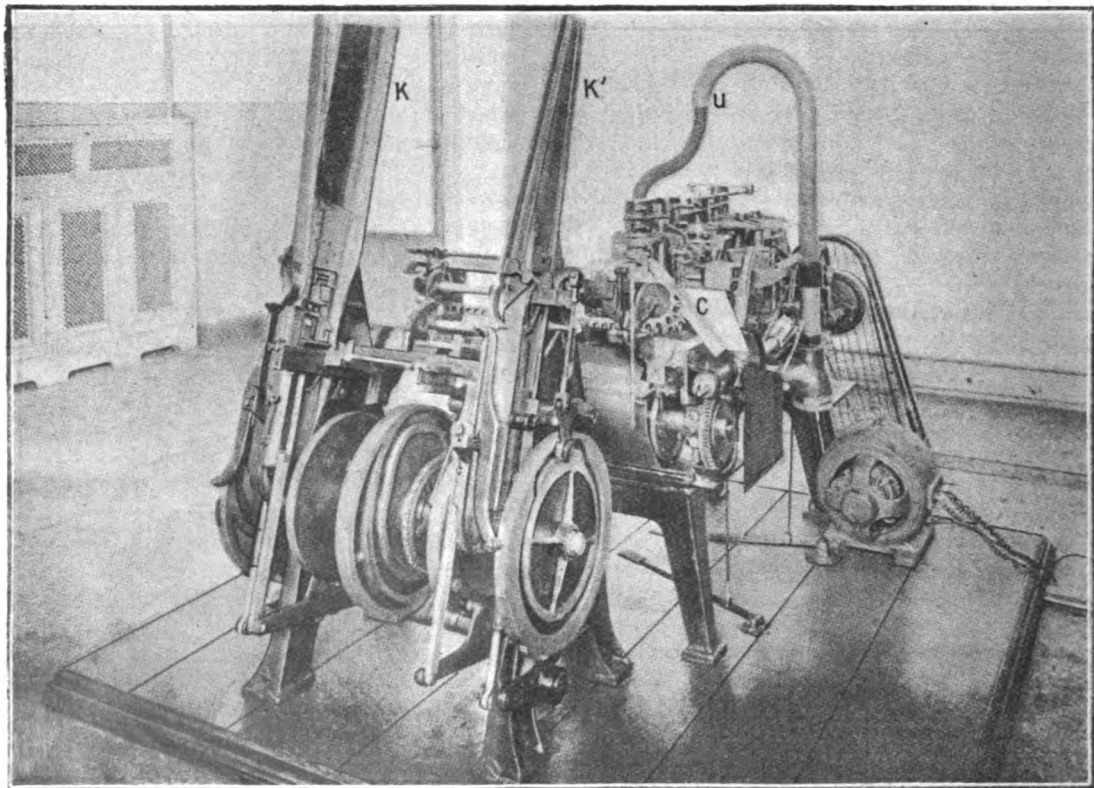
MACHINE A ROULER AUTOMATIQUEMENT LES CIGARES.
